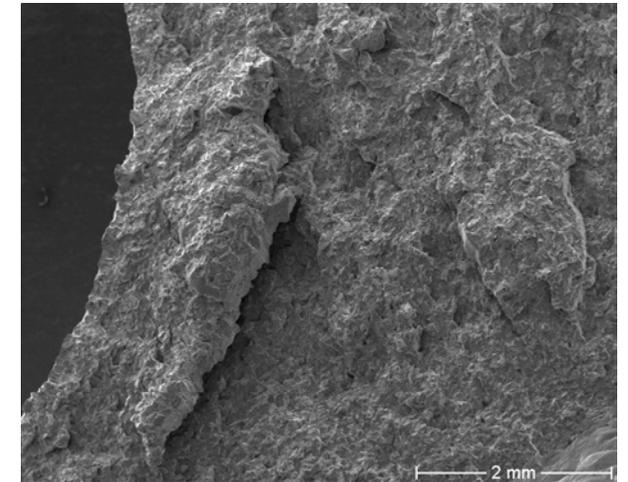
REM-Aufnahme einer Pleuelbruchfläche mit deutlich sichtbarer Materialabhebung
